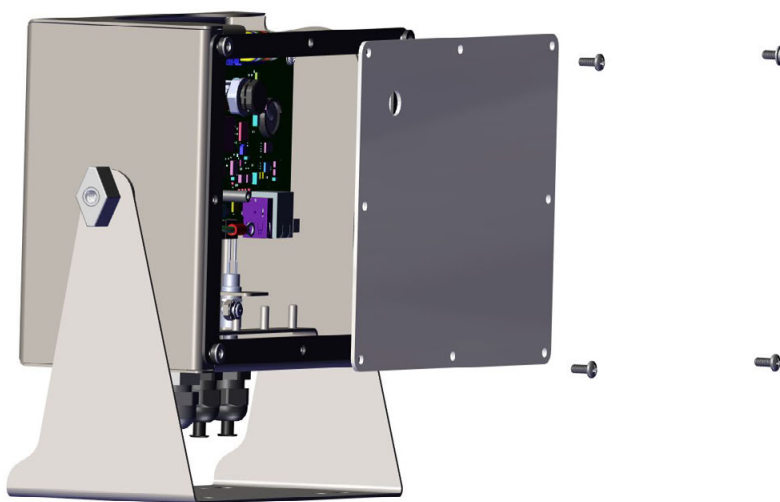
Desmontaje de la placa posterior del alojamiento universal
